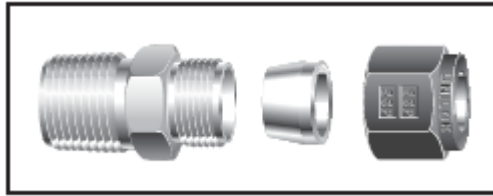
Componentes de los accesorios de conexión UNILOCK [34]
